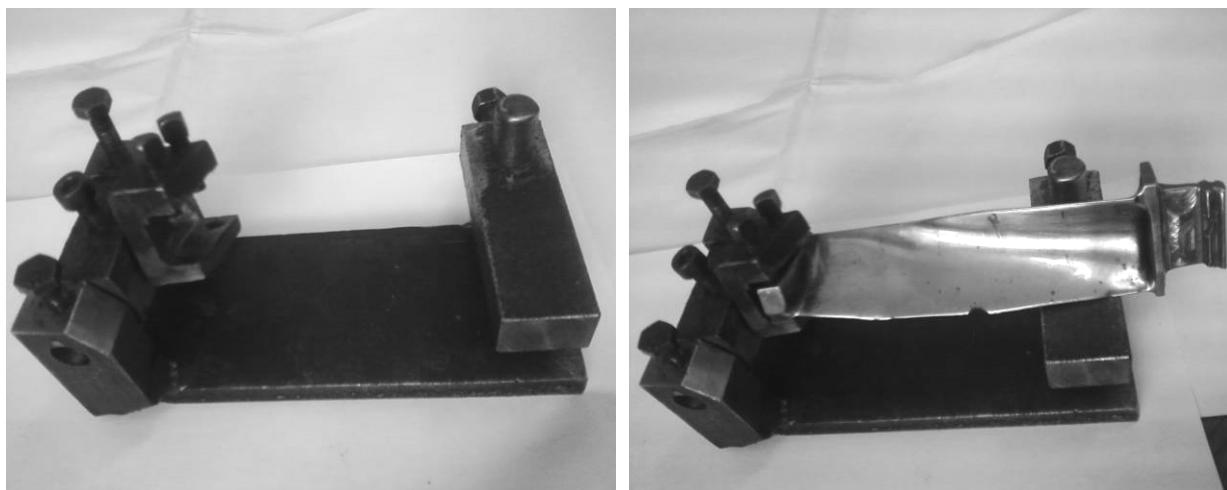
Конструкція наладки (установочного елемента) для робочої лопатки турбіни двигуна ТВ3-117
